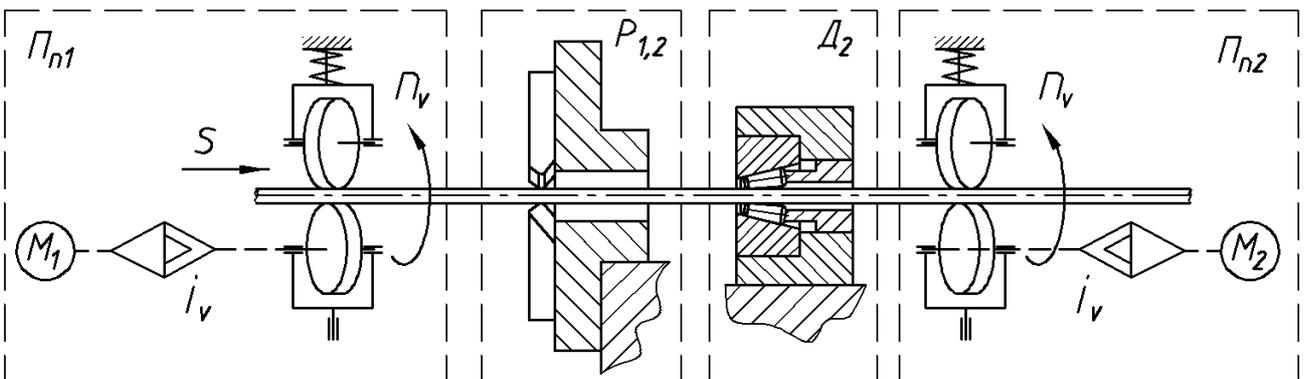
Конструктивная схема совмещенной обработки резанием и ППД роликами с продольно подаваемой и вращаемой заготовкой в сочетании с неподвижной резцовой головкой и обкатником
